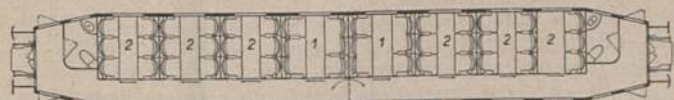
Grundriß eines Einheits-D-Zugwagens 1/2 Klasse.
